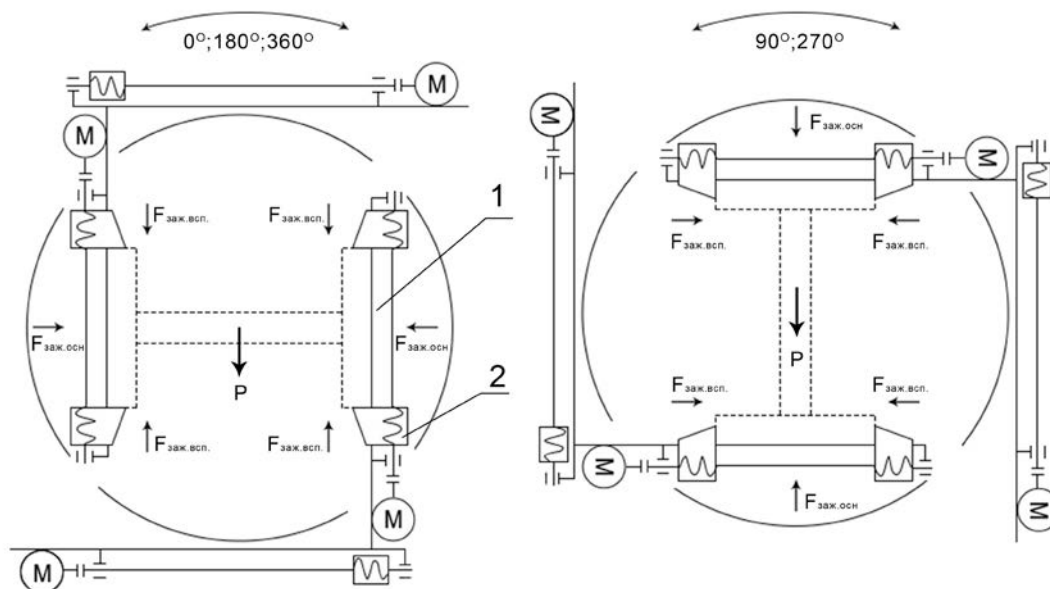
Схема зажатия заготовки поворотным порталом-кантователем:
